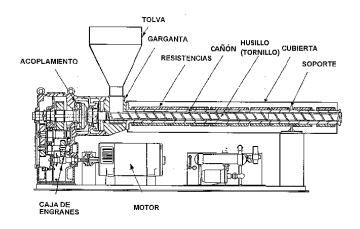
Esquema de corte de las partes que componen una extrusora mono-husillo típico.
